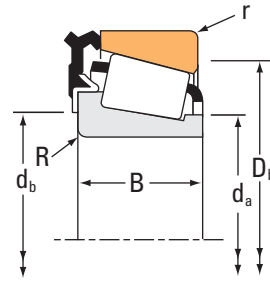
Контакт широкого торца внутреннего кольца и упорного заплечика вала (без контакта с уплотнением).
